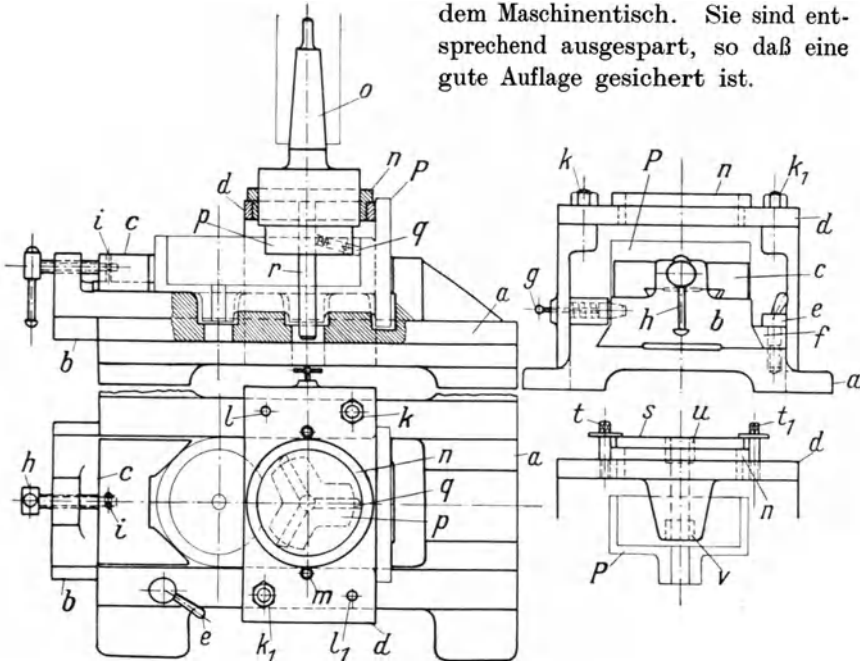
Das Ausbohren des Pumpenkörpers mittels Messerkopf.
